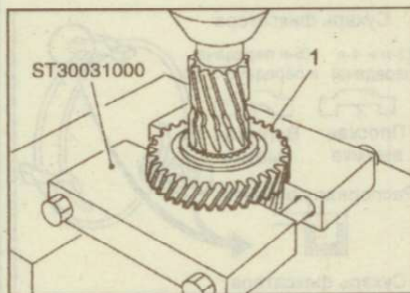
Снятие шестерни (1) 5-й передачи с первичного вала
